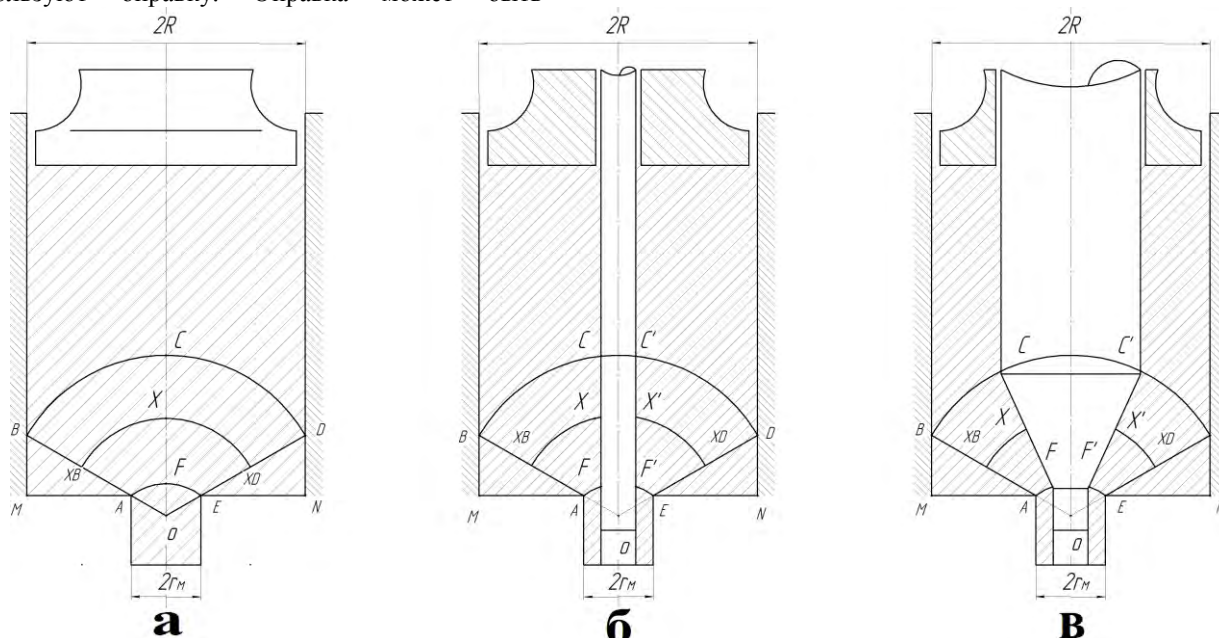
Схемы выдавливания заготовки без оправки (а), с цилиндрической (б) и ступенчатой (в) оправкой
